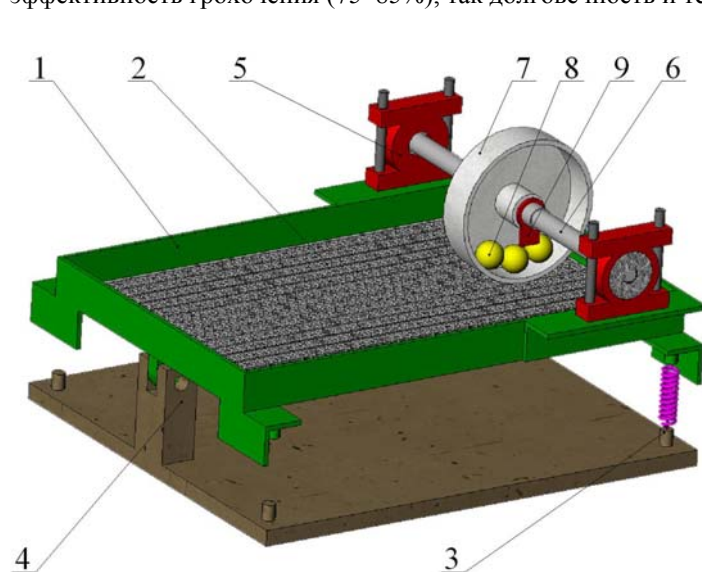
3D модель станда грохота с колебательно-вращательным движением короба
